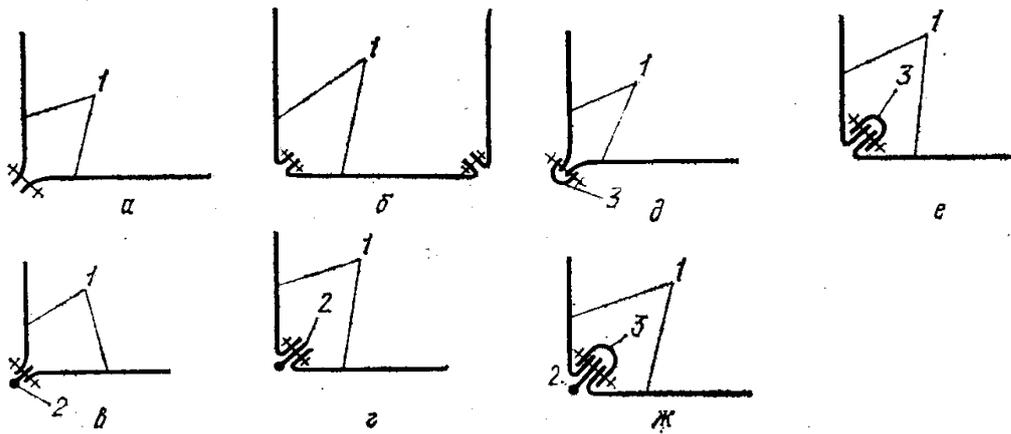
Варианты точного шва при соединении деталей: 1—материал верха; 2— кедер; 3—окантовка
